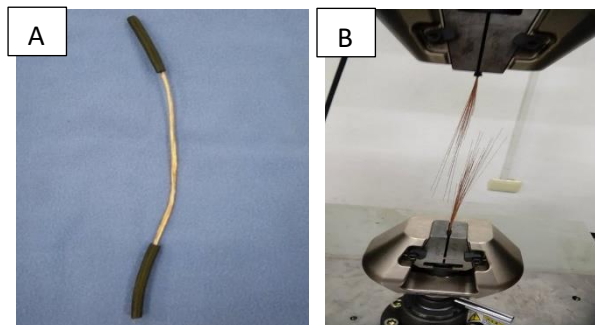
Cable base: A) Probeta de cable automotriz. B) Rompimiento de cable por fuerzas de tensión.
